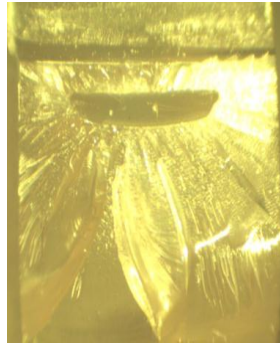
Superficie de fractura de una probeta con entalla incorrecta.
